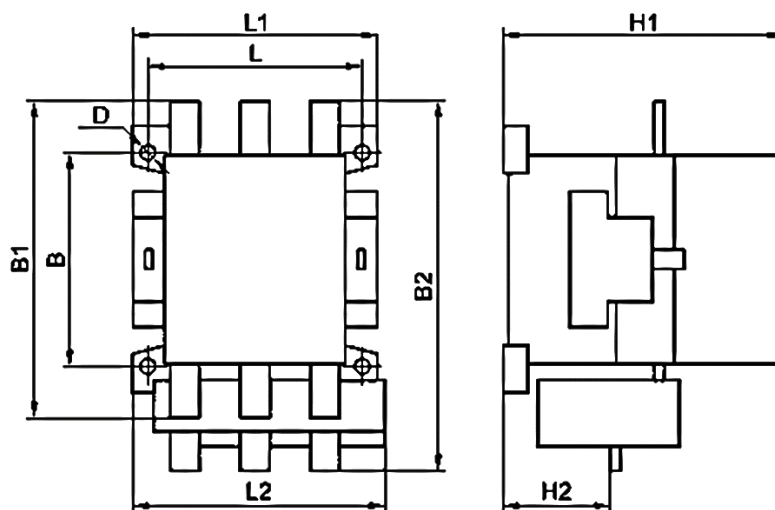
Пускатель нереверсивный ПМ12 100-250А
